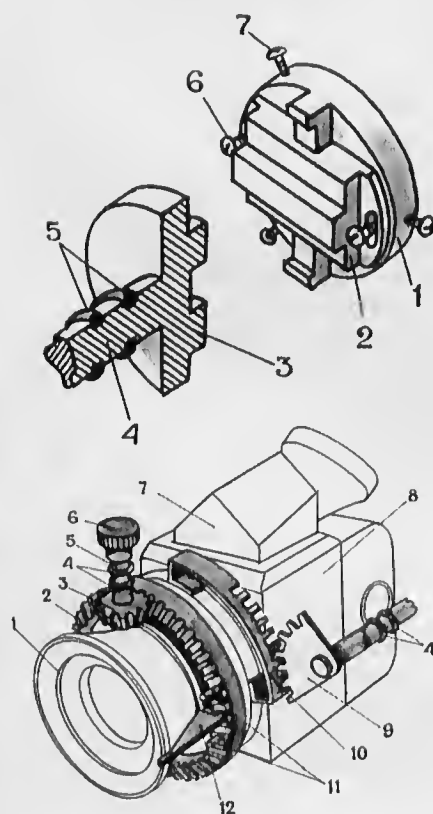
Общий вид механизмов изменения дистанции и диафрагмы: 1 — объектив; 2 — зубчатое колесо; 3 — шестерня; 4 — уплотнительное кольцо; 5 — ось механизма; 6 — рукоятка привода; 7 — оборачивающая призма; 8 — корпус «Салюта»; 9 — ось привода с зубчатым сектором; 10 — привод к диафрагме объектива; 11 — стопор; 12 — поводок объектива.
